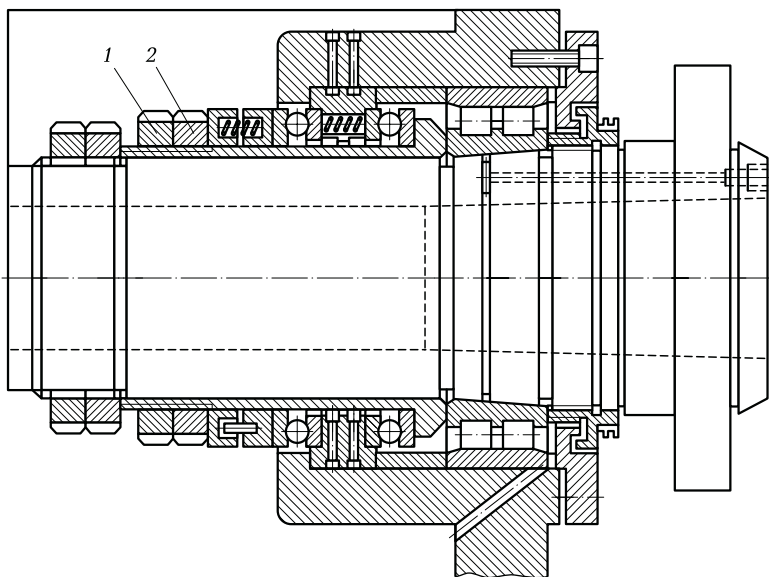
Регулирование радиального зазора в подшипнике передней опоры шпинделя токарного станка:
